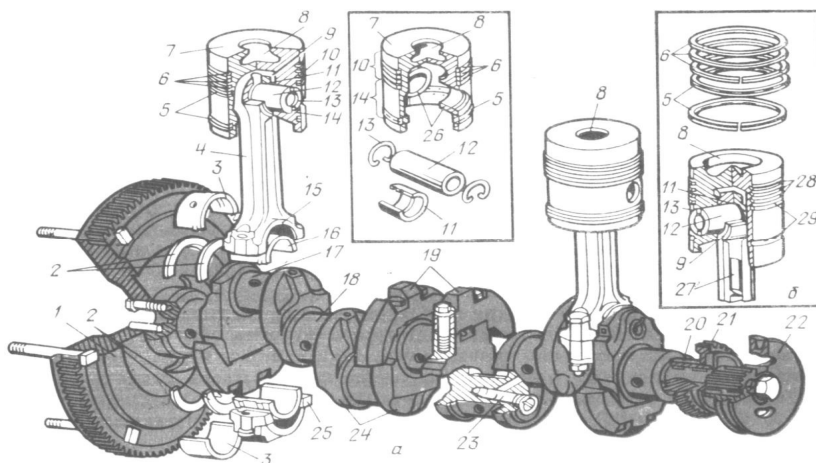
Деталі кривошипно-шатунного механізму дизеля Д-240:
